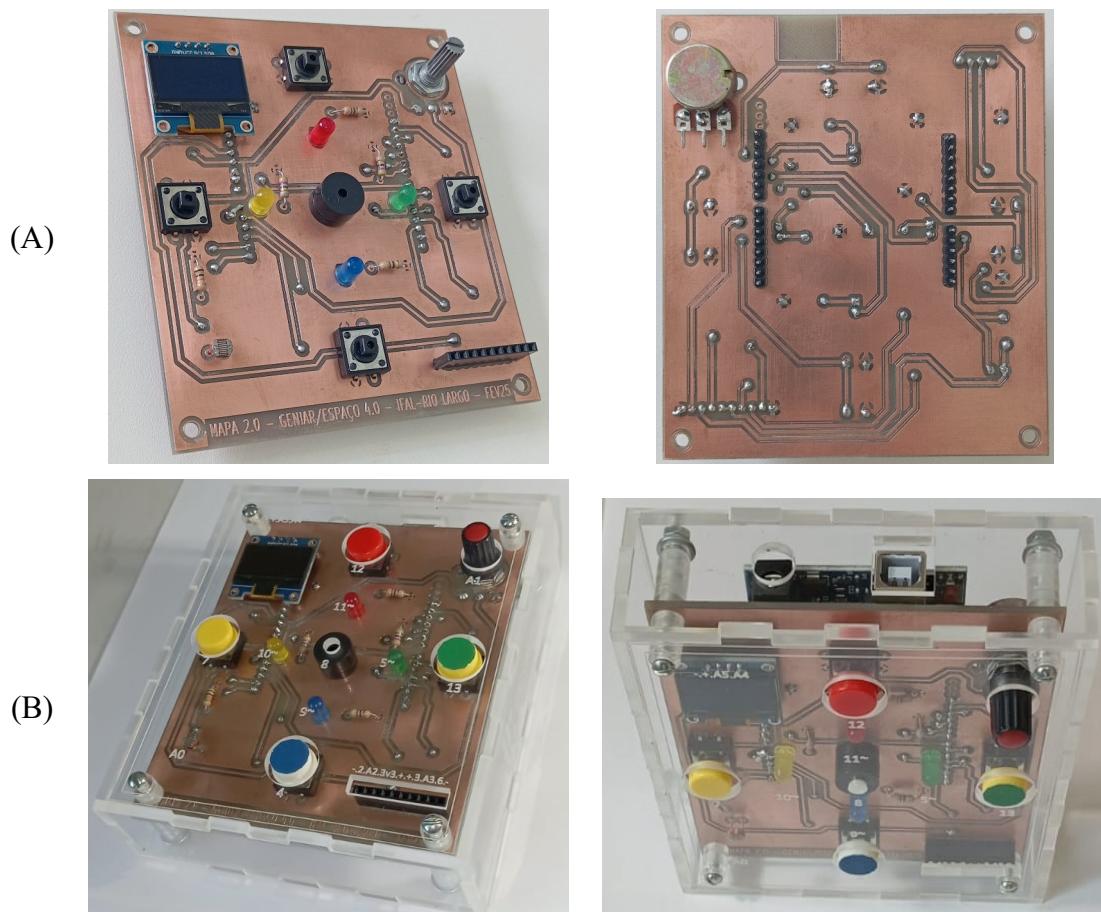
(A) Componentes soldados na placa de circuito impresso. (B) MAPA finalizado.
